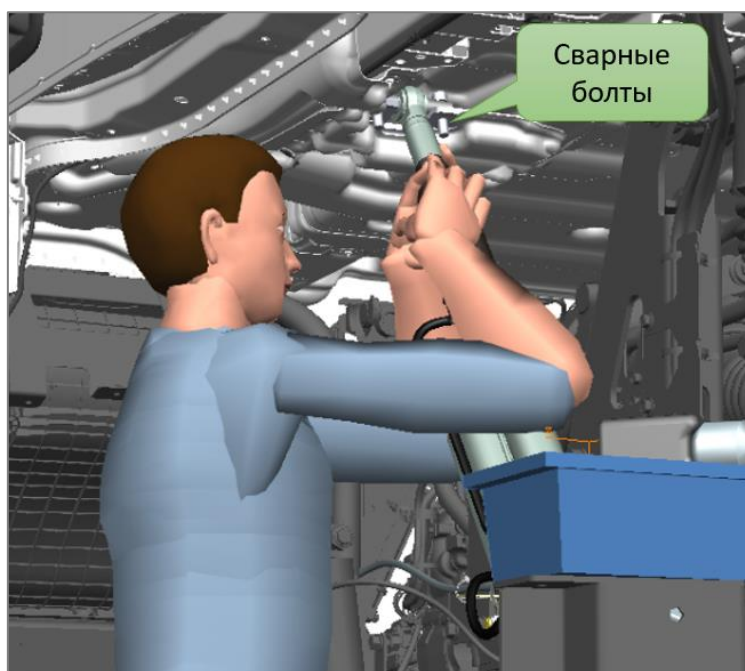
Процесс установки гидроцилиндра в сборе с болтами
